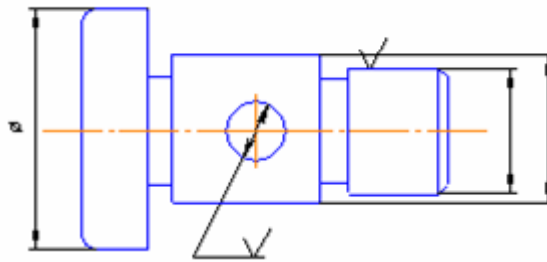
Нанесение обозначений шероховатости на чертеже
